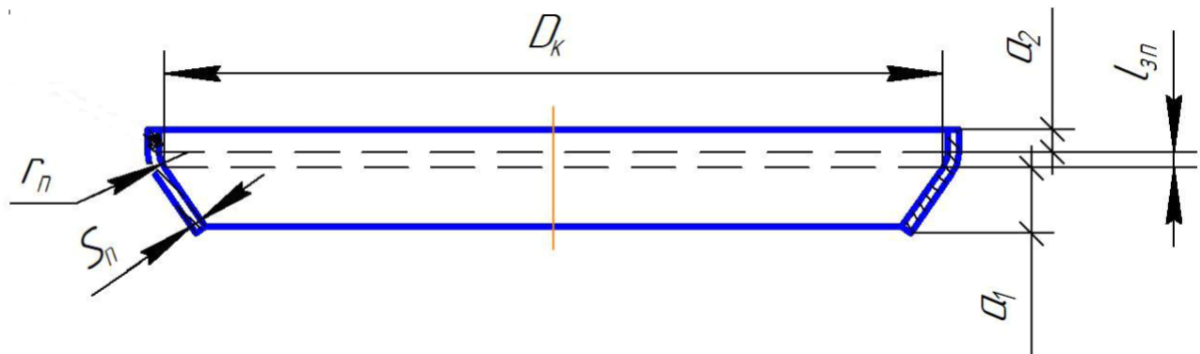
З'єднання циліндричної обичайки з тороїдальним переходом.
